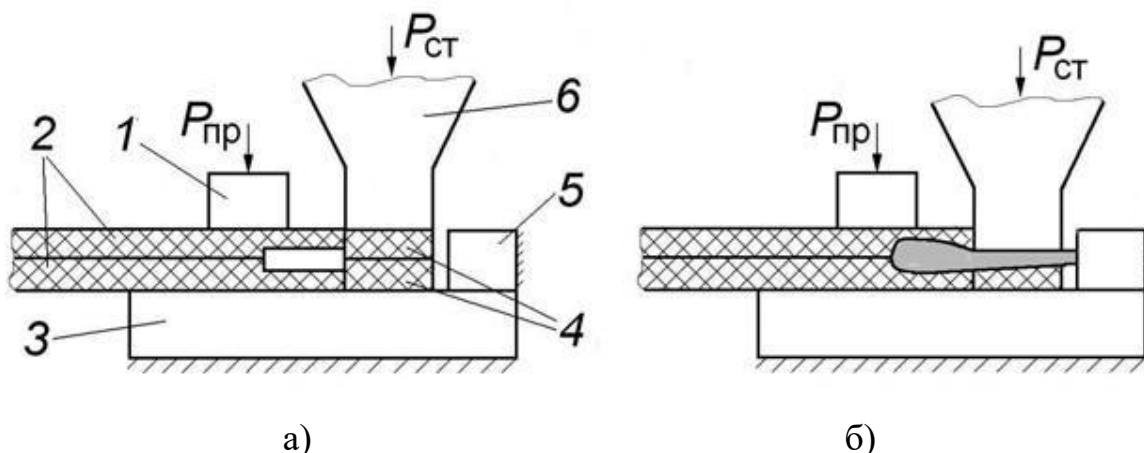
Схема зварювання витиснутим розплавом: а-початок зварювання; б-закінчення зварювання. 1-прижим; 2-деталі; 3-опора; 4-технологічні частини деталей; 5-упор; 6-хвилевід. $P_{пр}$ - зусилля притиску; $P_{ст}$ - статичне зварювальне зусилля. δ -товщина, b -ширина технологічного зазору.
